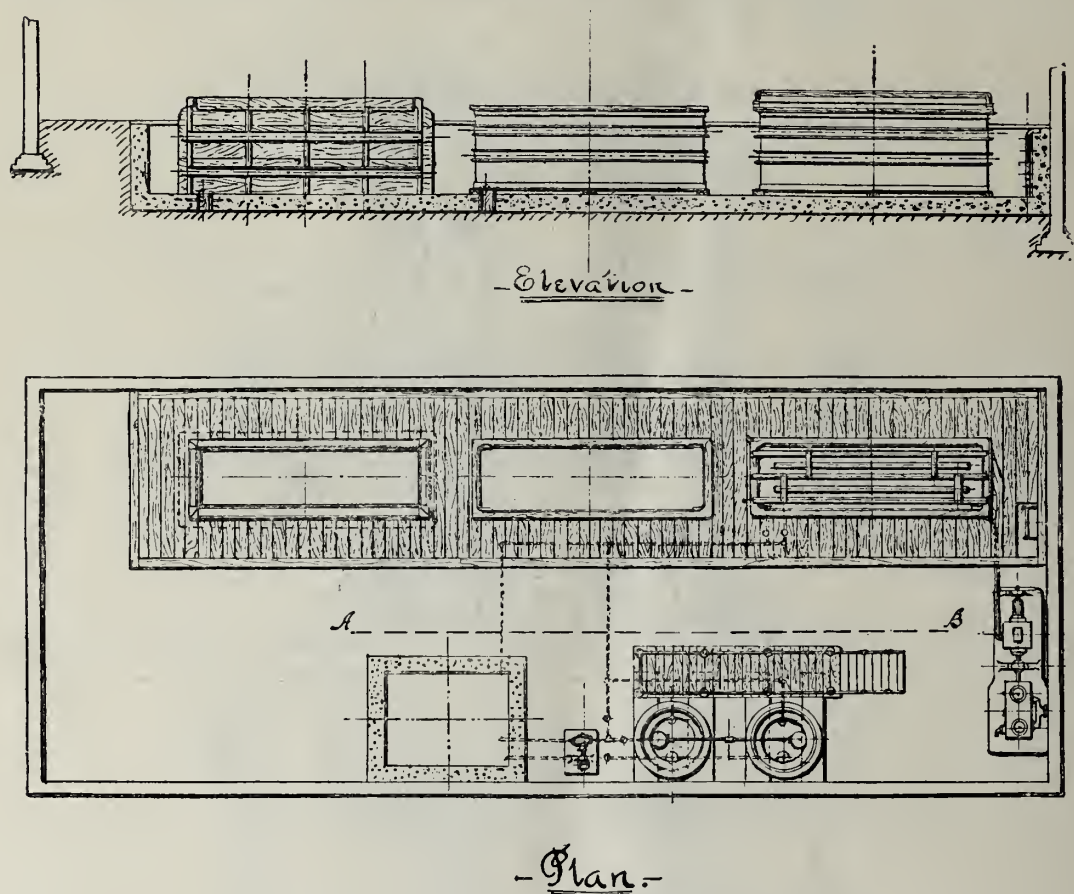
et 134. — Schéma de l'installation d'électrozincage de la « Germania Shipbuilding and Engineering Co ».
